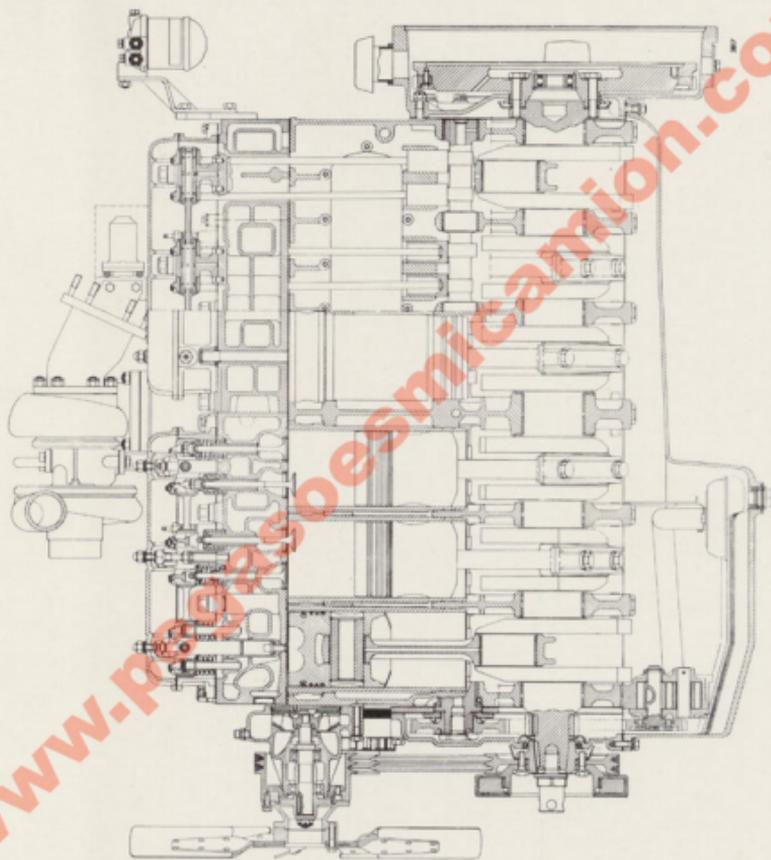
Motor 9156 y derivados. Sección longitudinal (Montaje HASTA)
